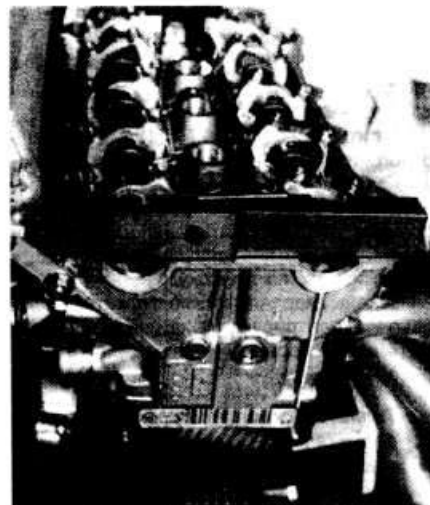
Блокировка распределительных валов в положении установки привода механизма газораспределения приспособлением BMW 11 32 40
